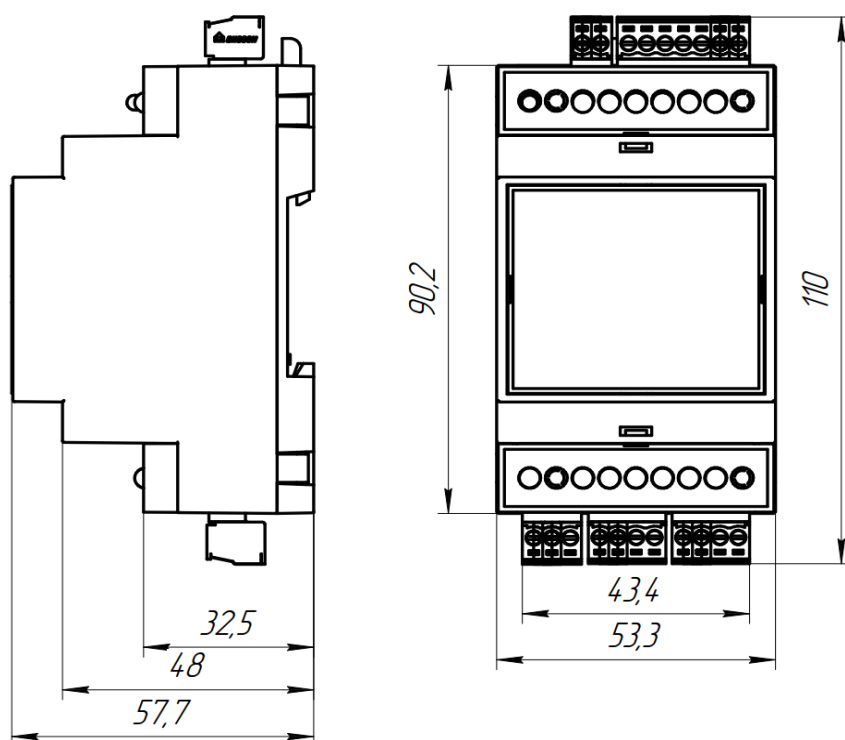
Габаритные и присоединительные размеры контроллера
